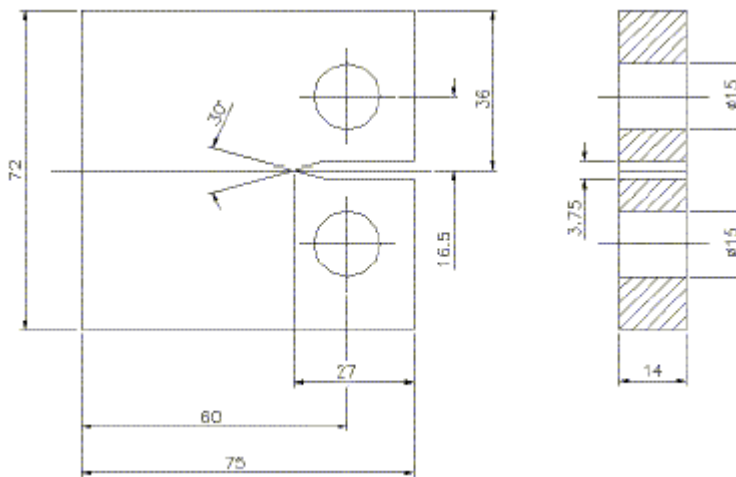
Dimensões (mm) do corpo de prova C(T) para os testes de propagação de trinca por fadiga.
